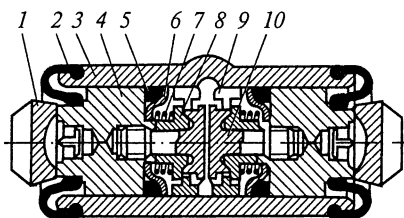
Задний колесный тормозной цилиндр автомобилей ВАЗ:
